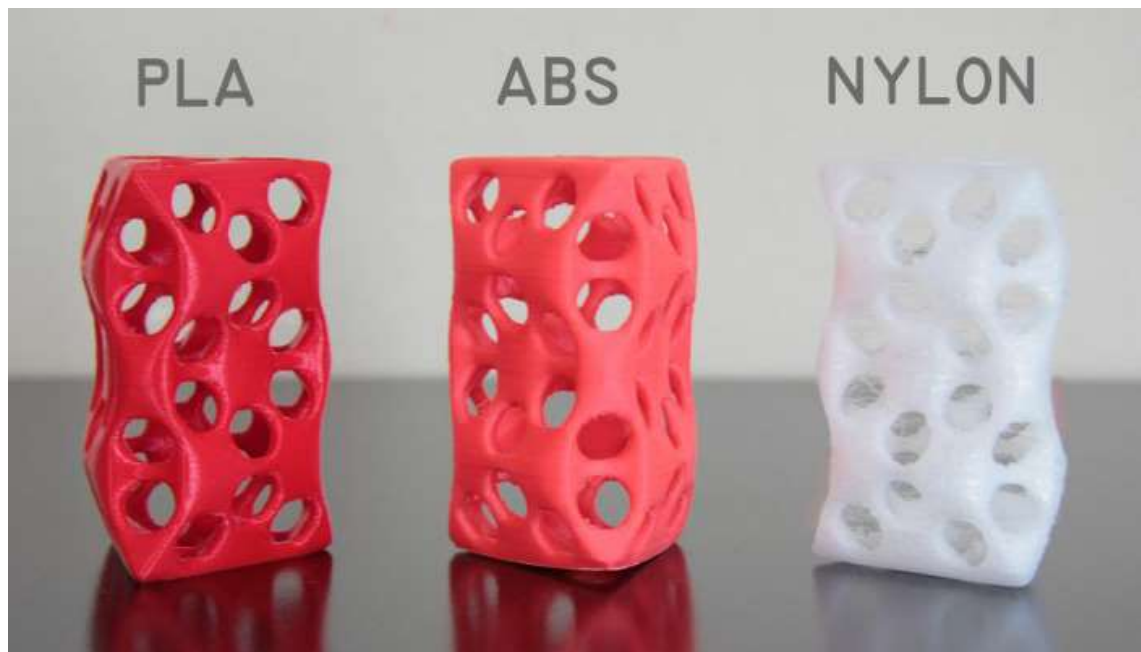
Пластмаси доступні для 3D друку та фрезерування з ЧПУ
